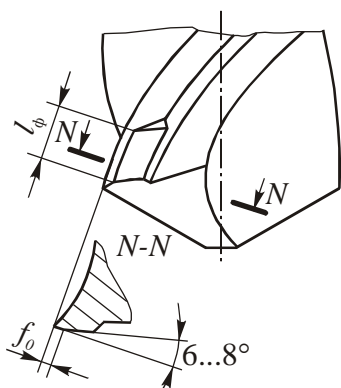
Подточка калибрующей ленточки спирального сверла
